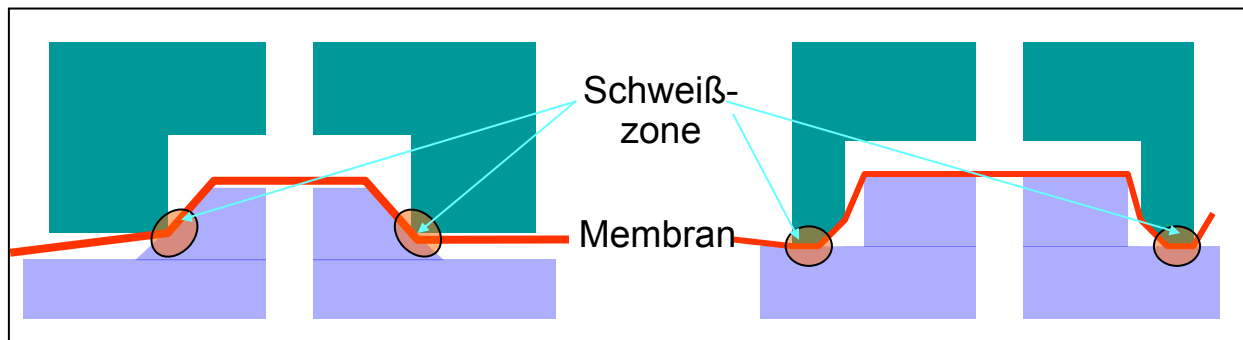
Möglichkeiten, Membranen mit den Gehäusen zu verschweißen
